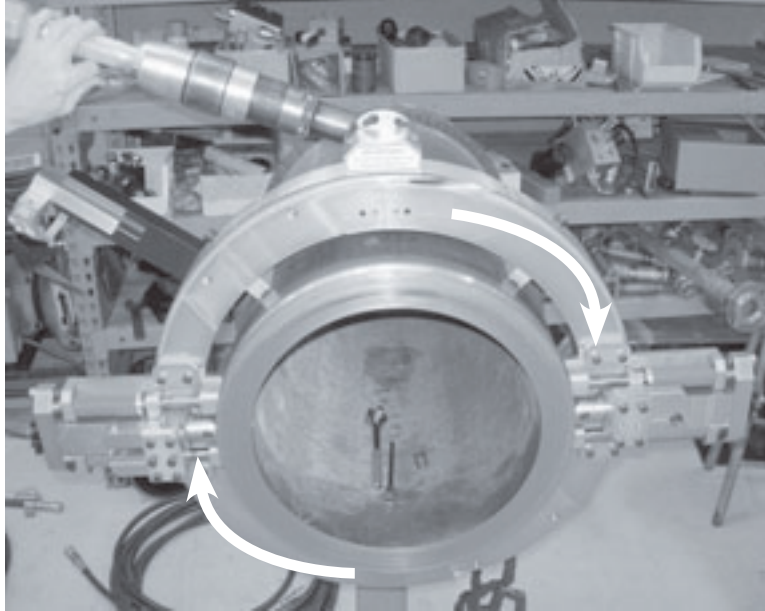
Faites tourner lentement la machine LCSF d'un tour complet pour régler les positions des plateaux.
